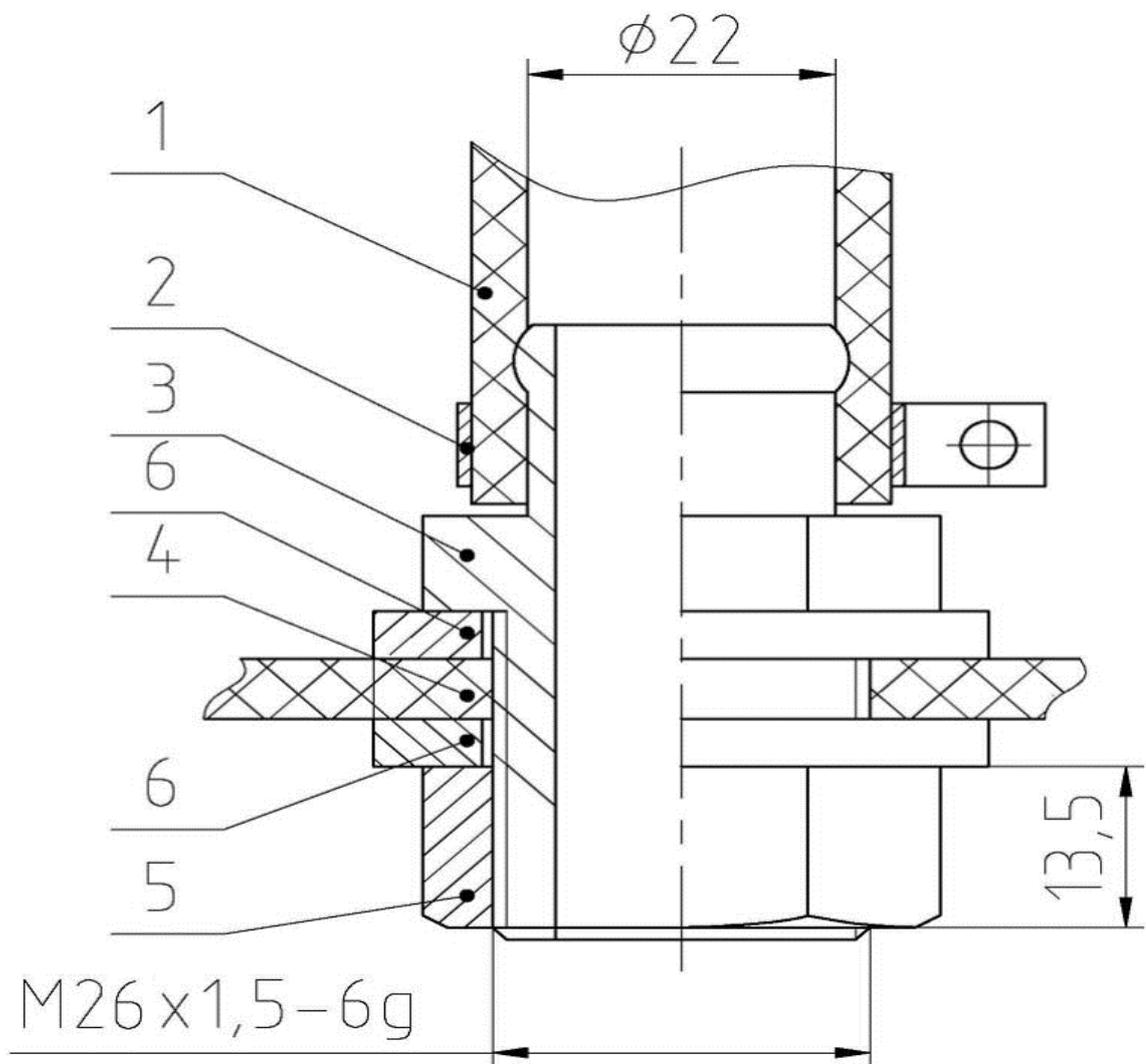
Установка Штуцера 7408-3509273 в патрубок 5320-1109445.
